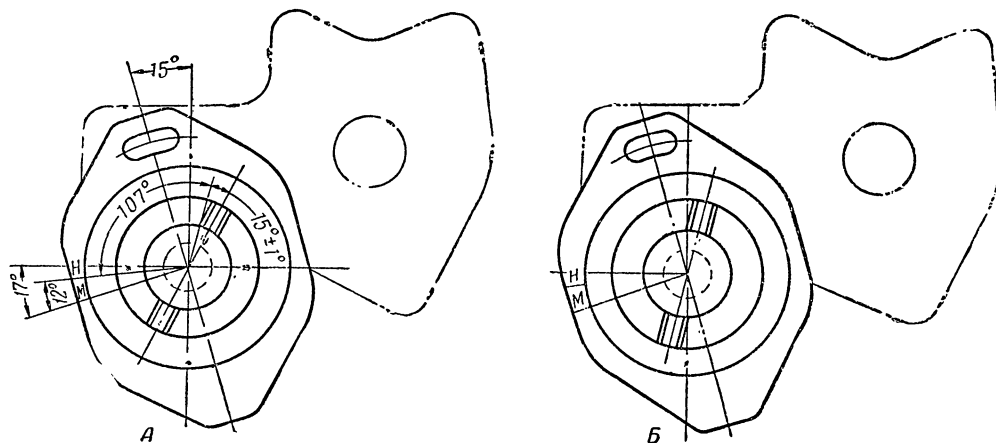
Установка корпуса распределительных шестерен по меткам:
